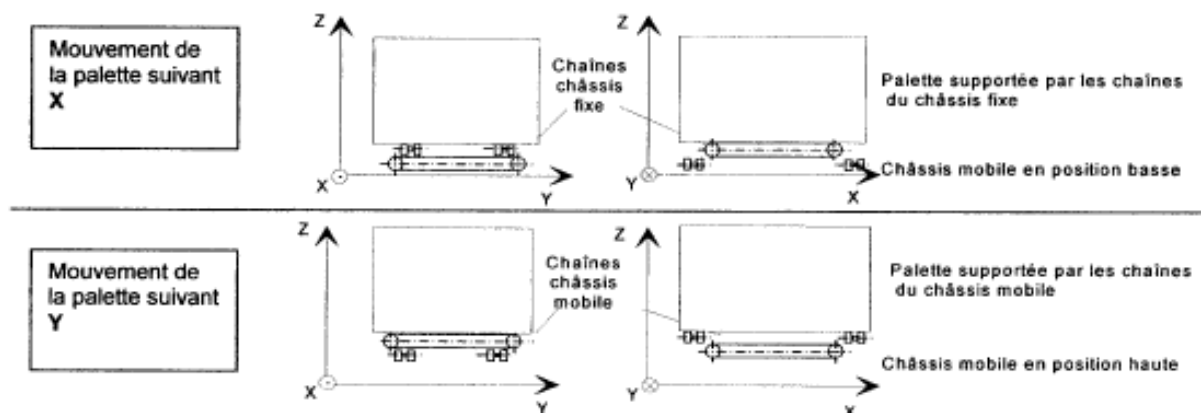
INTERVENTION DU SYSTEME SUR LA PALETTE
